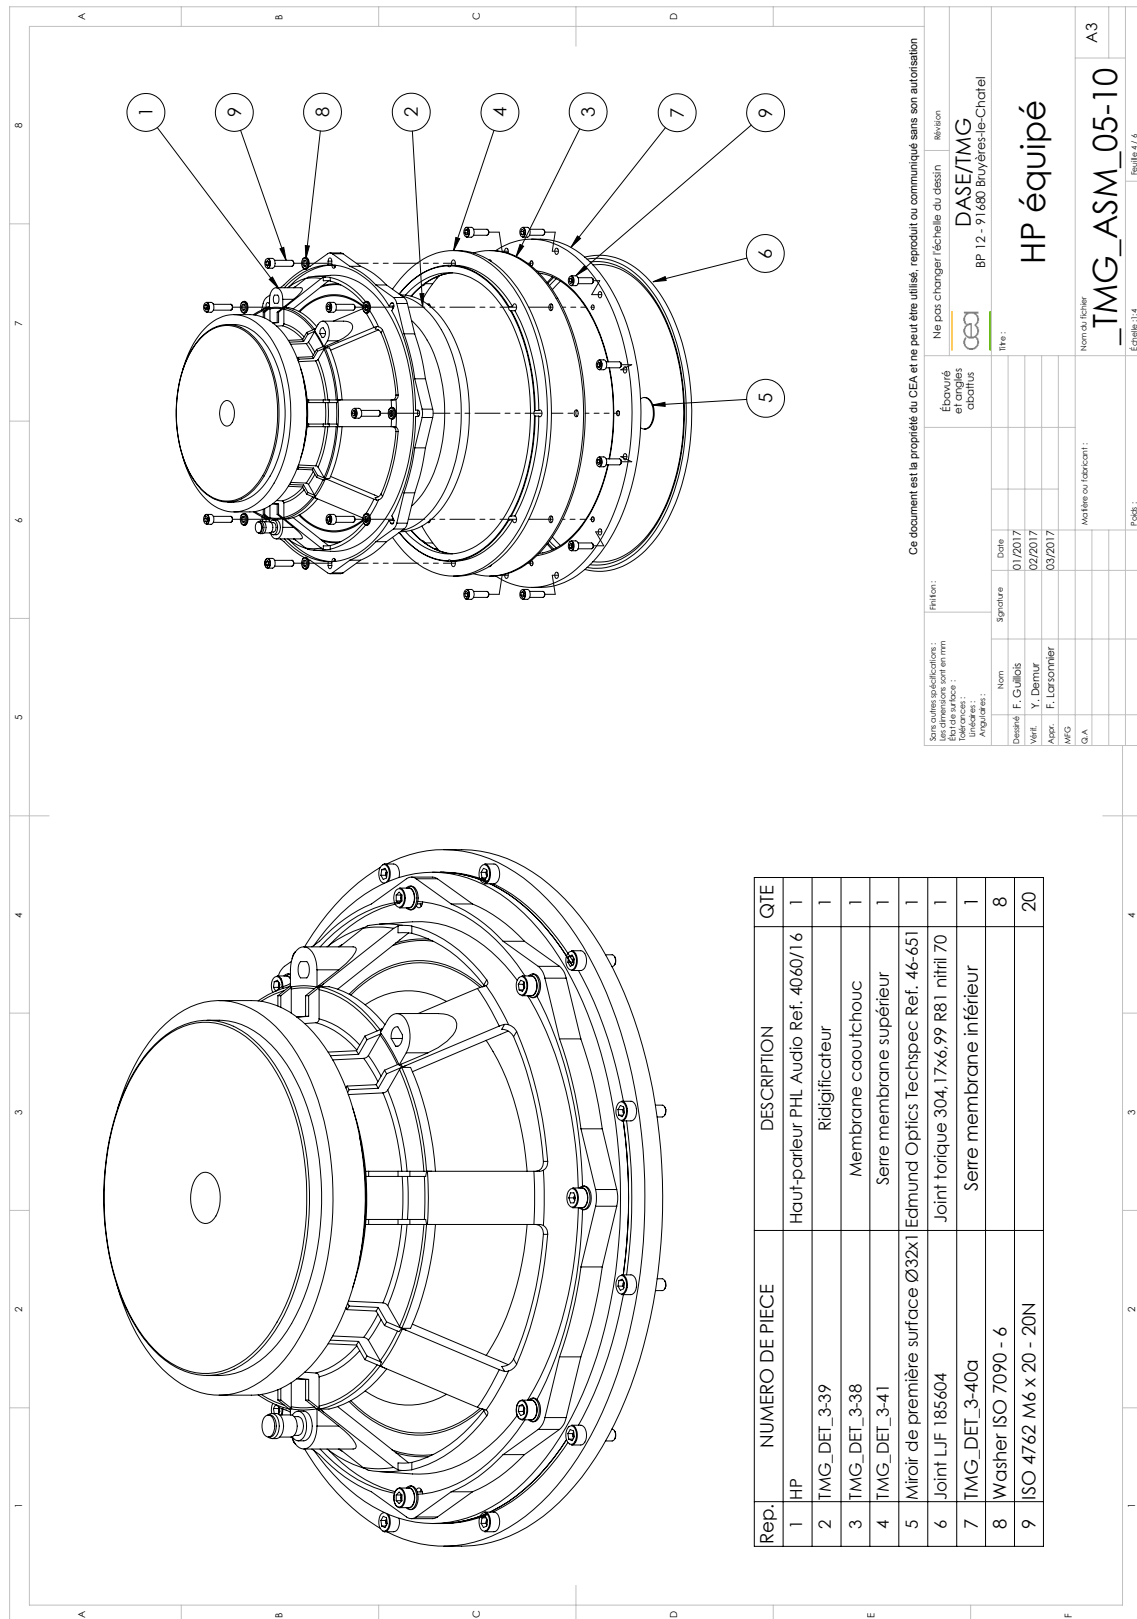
Étalon primaire : plan du haut-parleur équipé.
